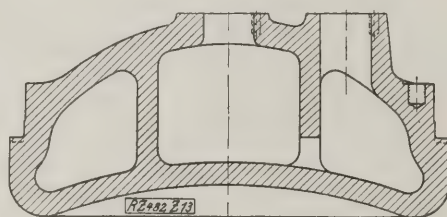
Neuer oberer Zylinderdeckel 1:15.
